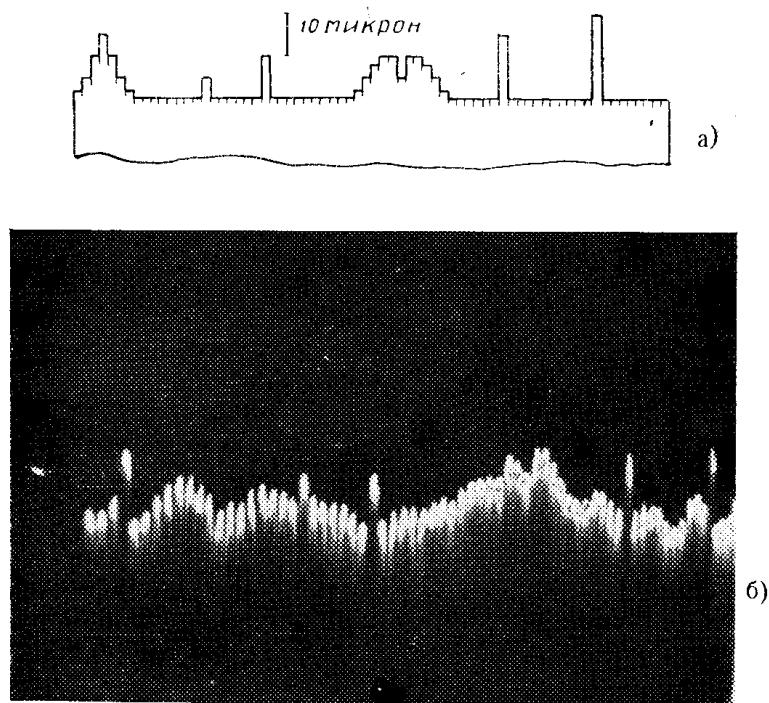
а — запланированный профиль коллектора, б — реализованный профиль
